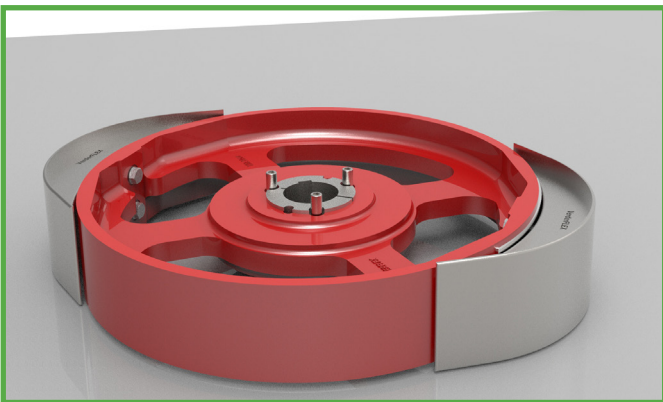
Rotorbaken auf den Rotor montieren (Schritt 2)
